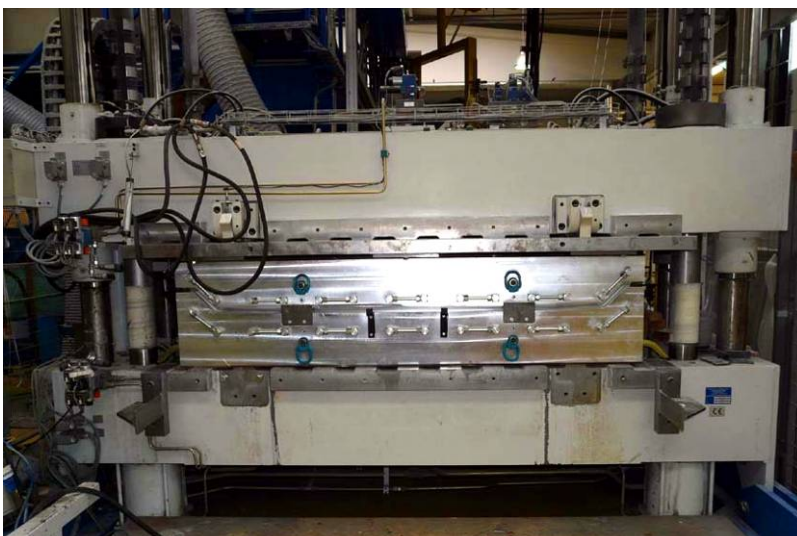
Werkzeug „Bodenplatte I“ gerüstet auf Formenträger
